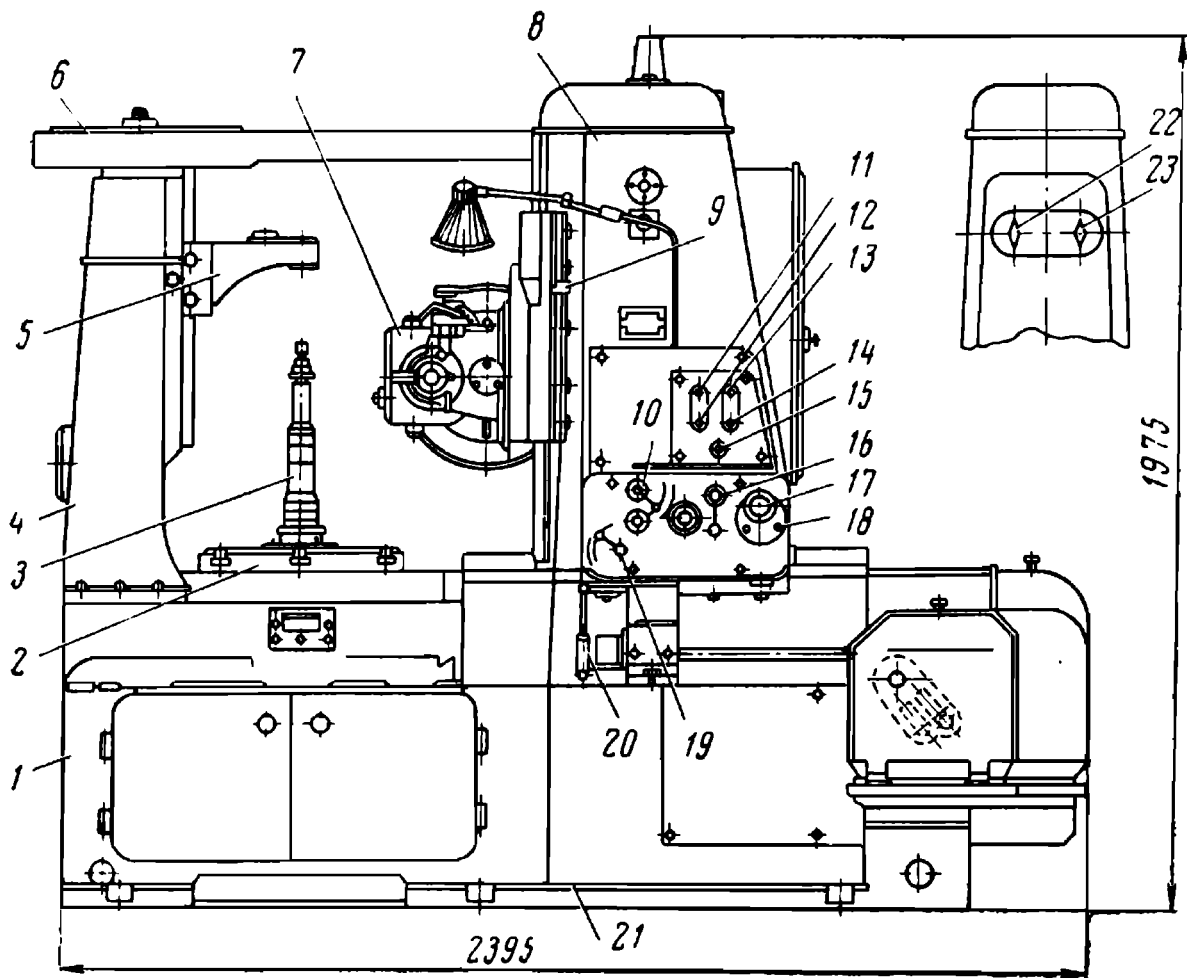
Схема устройства зубофрезерного станка 5Д32
